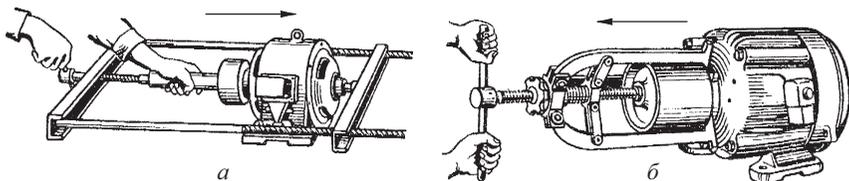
Насадка и снятие шкива с вала электродвигателя:
